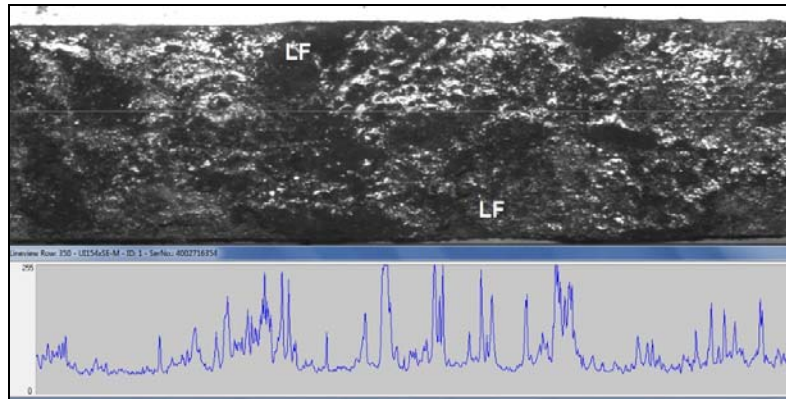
Superficie la probeta con soldadura MMA a compresión.
